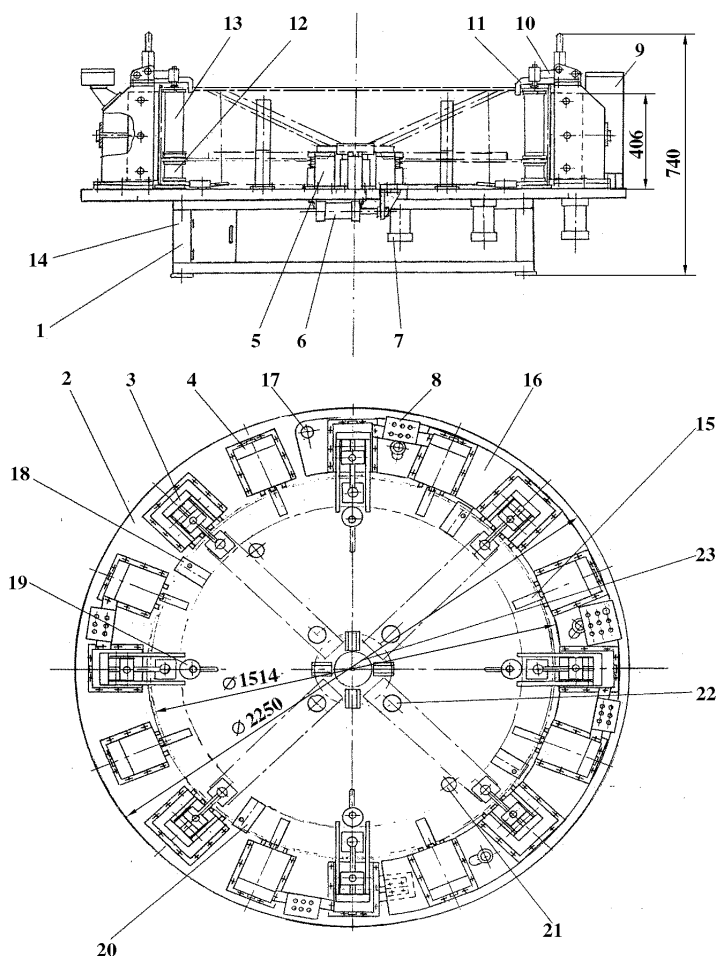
Конструкция кондуктора для сборки и сварки остова барабана
